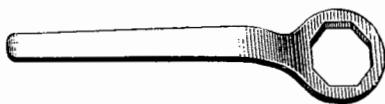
Ключ накладной 47001-1-011МД для гайки дет. 233-12-171, 172 валов коробки передач
